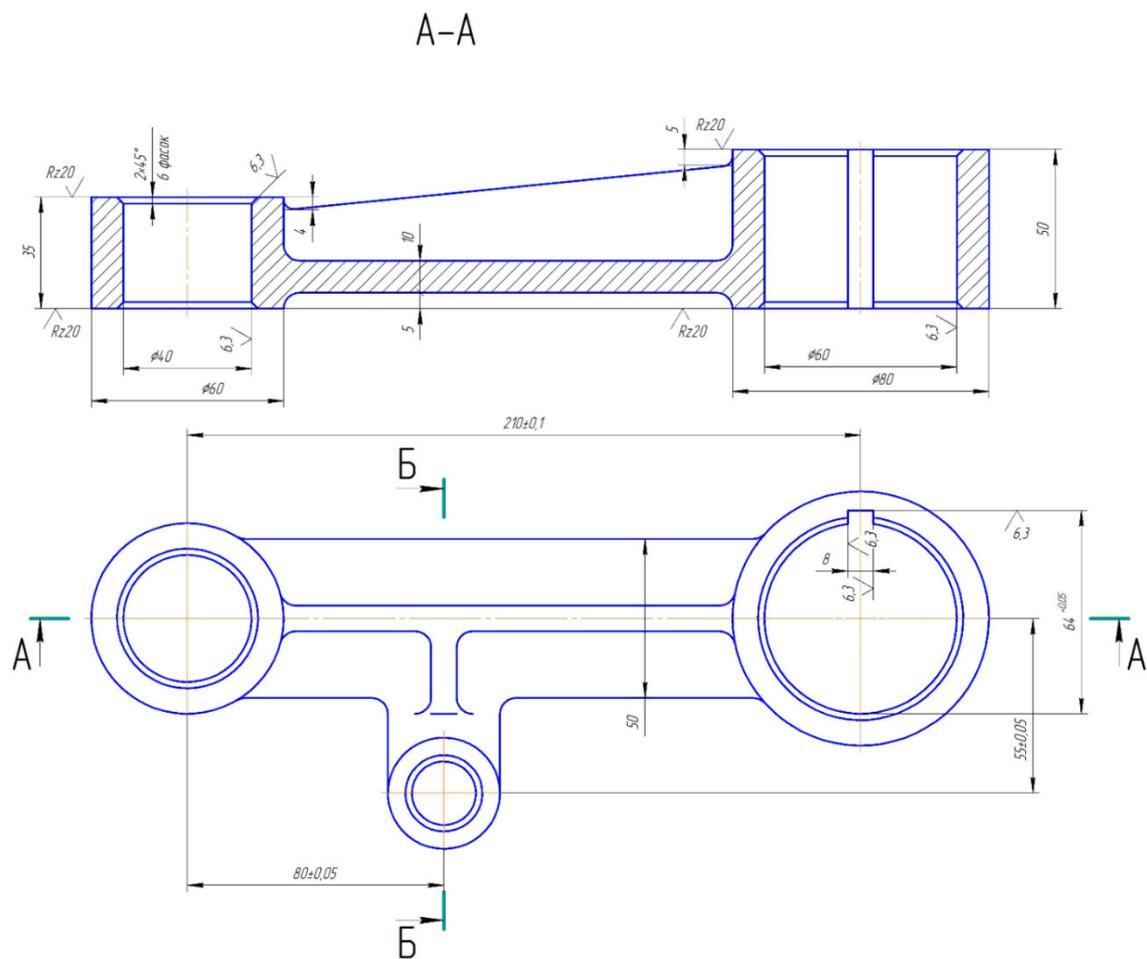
Эскиз детали «Рычаг двуплечий»
